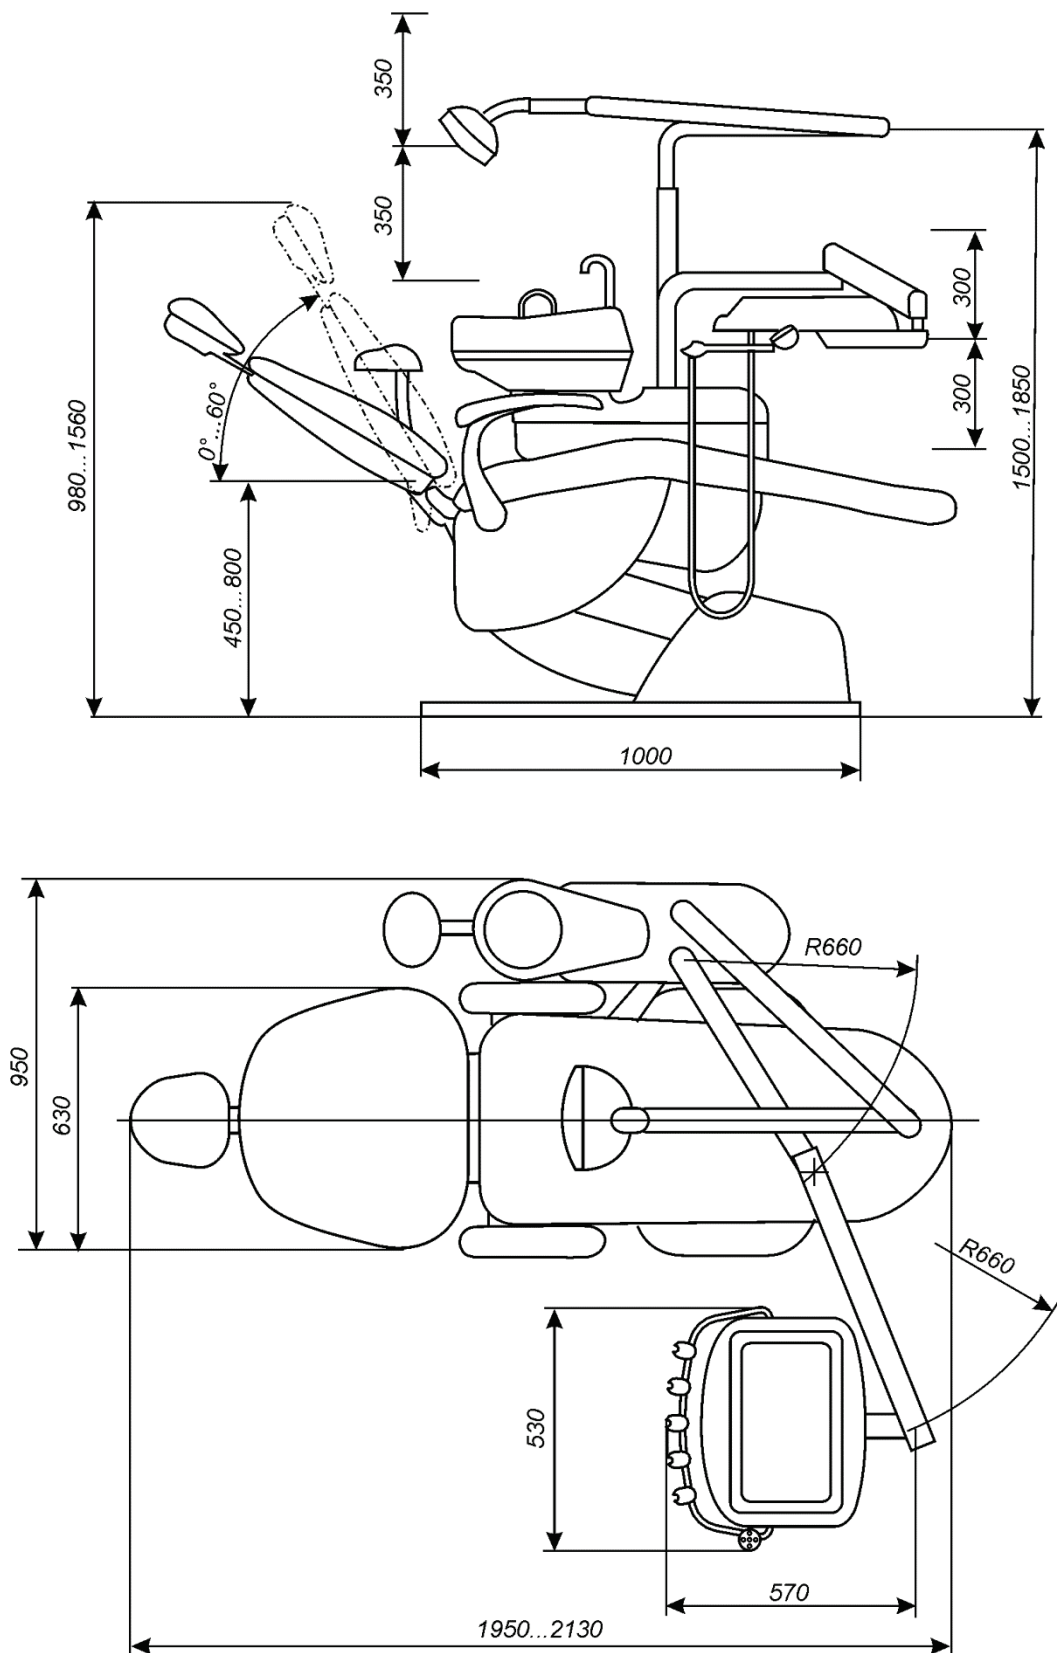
Габаритные размеры стоматологической установки ДАРТА с креслом Дарта 1600 и блоком управления наконечниками с нижней подачей
